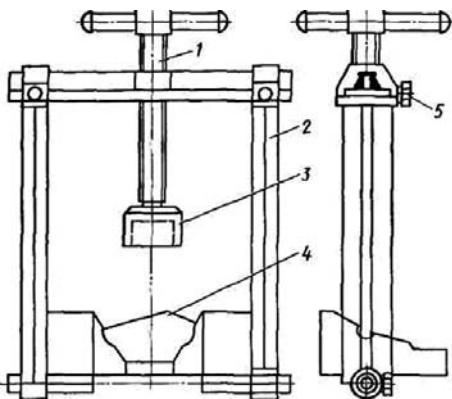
Приспособление для разборки карданных шарниров: 1 — винт; 2 — стойки раздвижные; 3 — стакан; 4 — опорная призма; 5 — фиксатор
